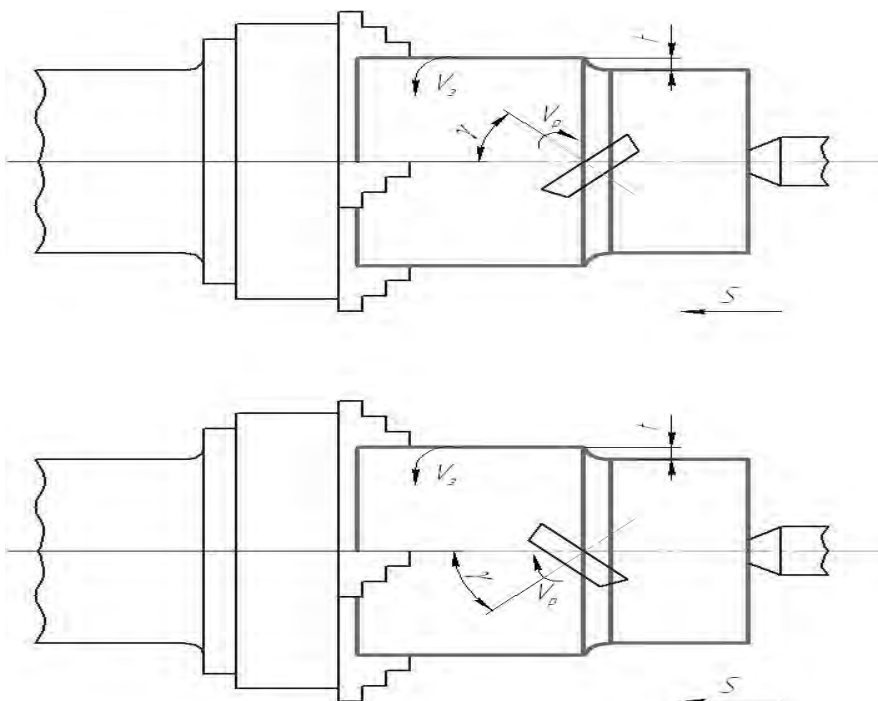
Схемы установки чашечного резца по оси обрабатываемой заготовки
